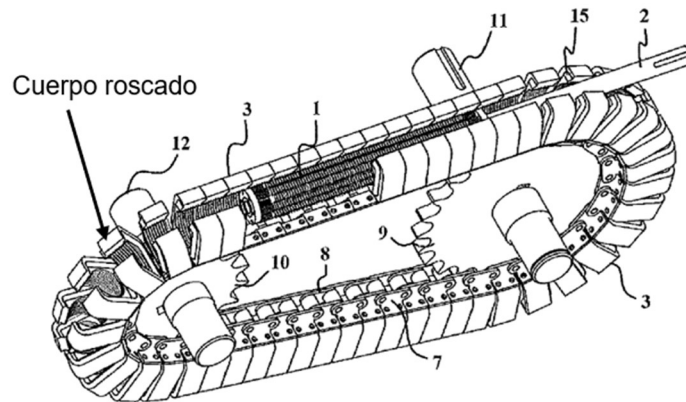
Esquema del ensamble del reductor integrando el tornillo impulsor de rodillos, (RVICR-1) [4]
